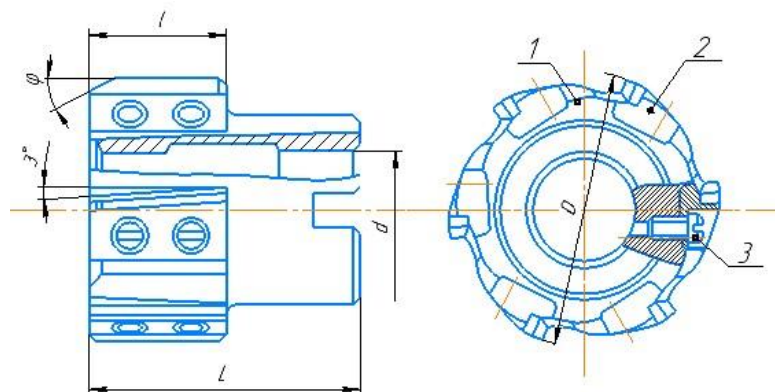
Збірна насадна розвертка з привертними твердосплавними ножами
